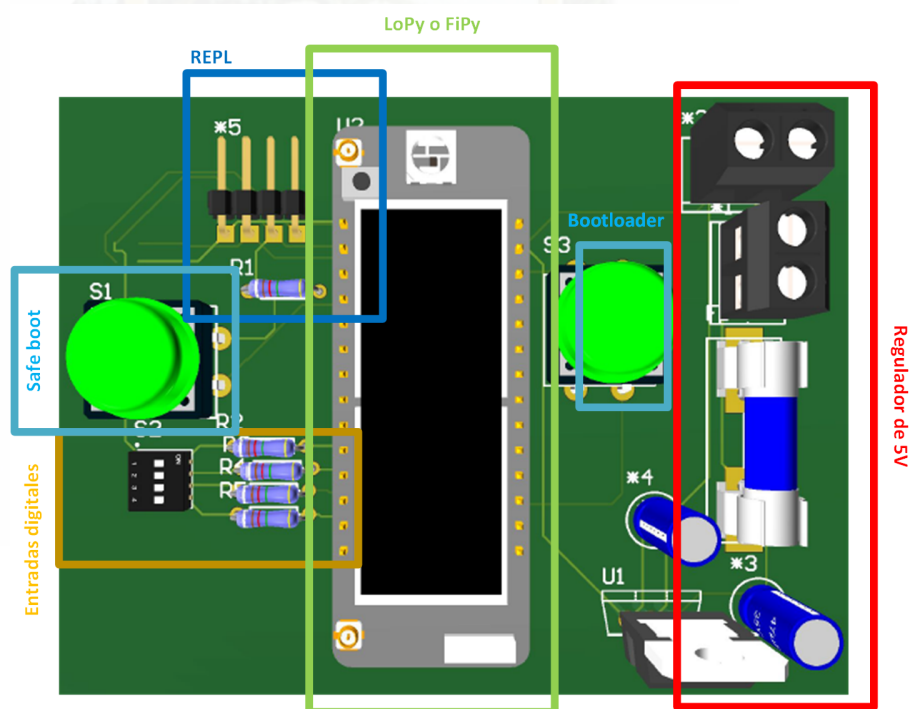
Diseño esquemático del PCB de control del nodo ancla.
